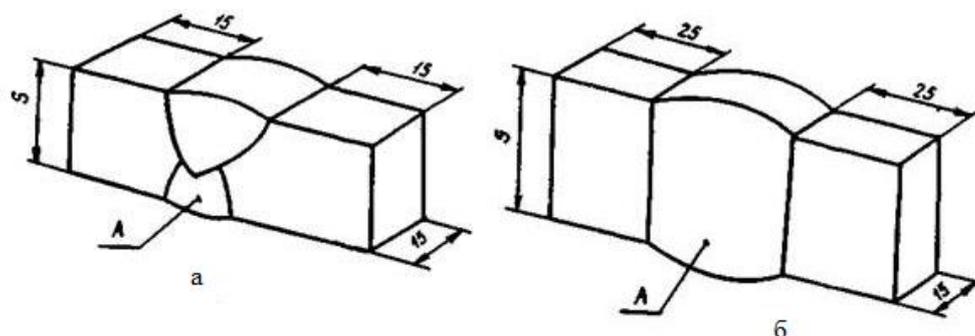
Образец сварного соединения для макроисследования:
